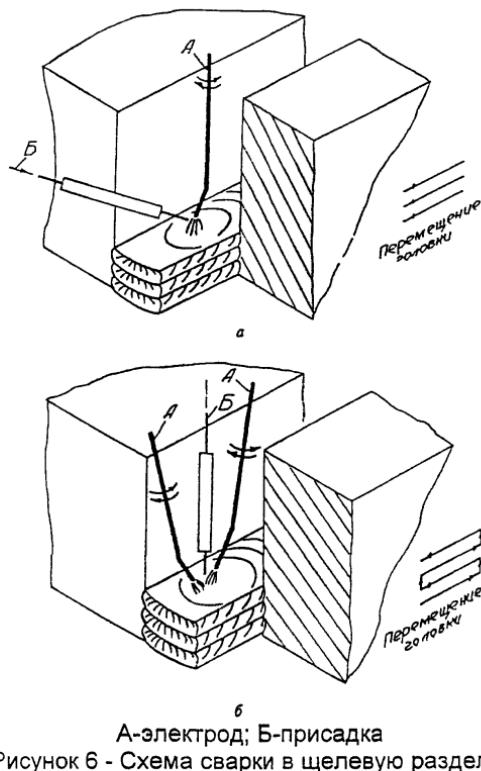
Схема сварки в щелевую разделку
